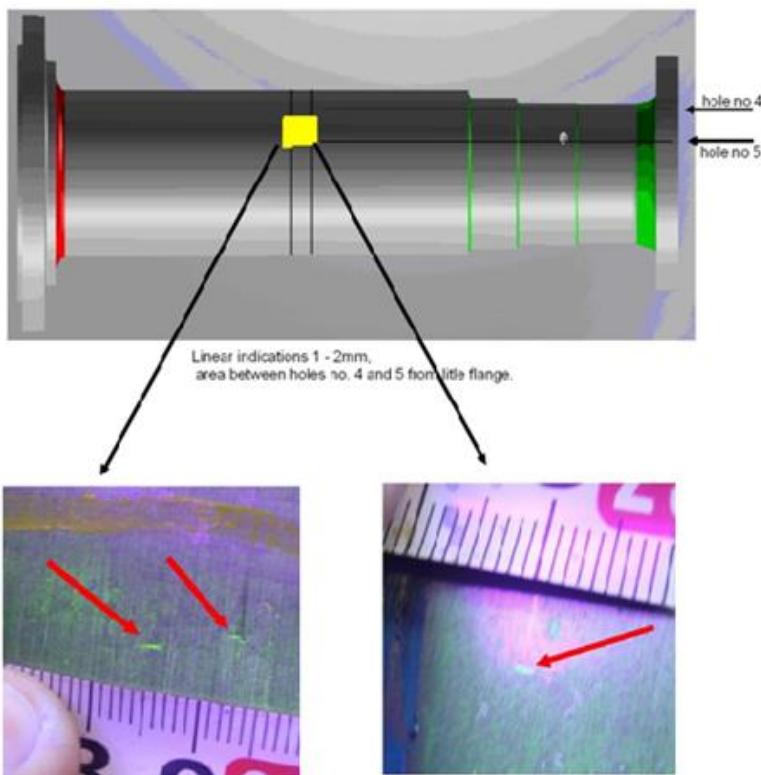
Examinare PM- arbore rotor turbină IP, tip F1C 330MW
